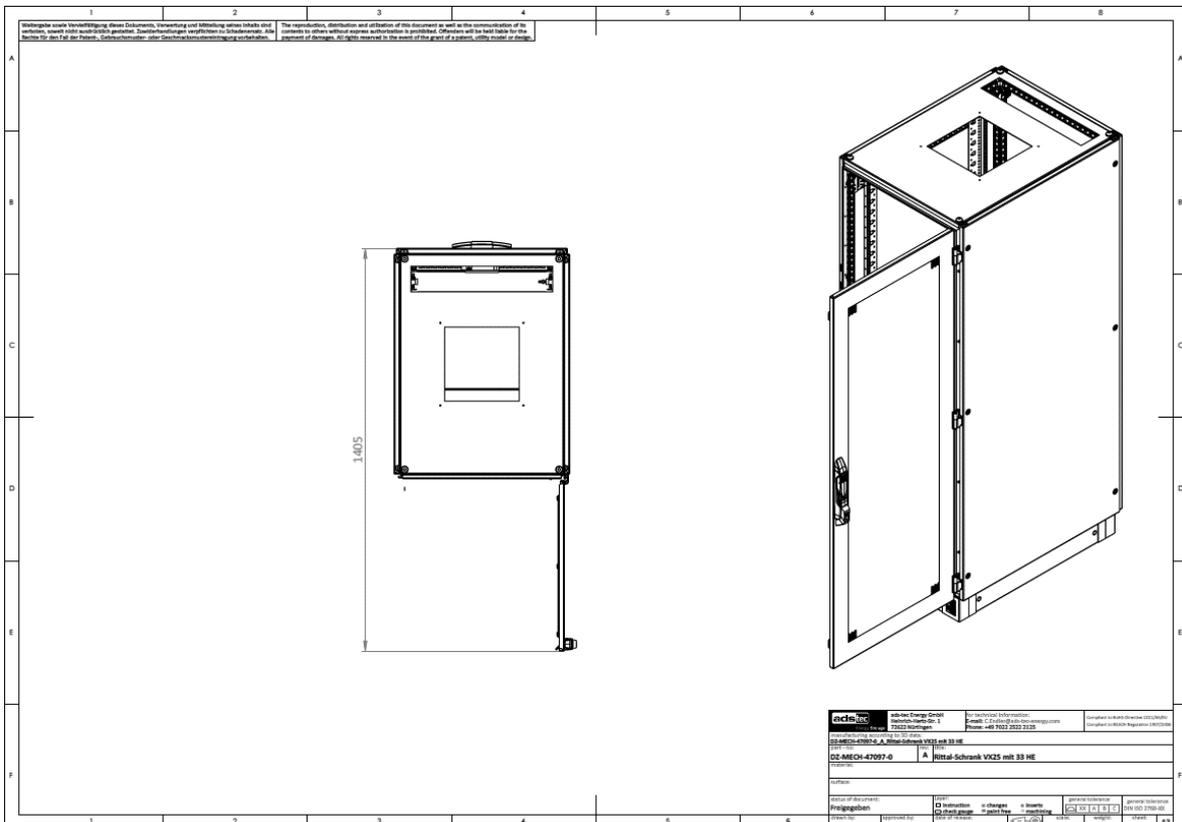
Konstruktionszeichnung Schrankgehäuse V1.0 - Blatt 2
